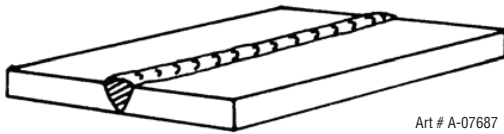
Soudure à plat, bout à bout depuis le haut
